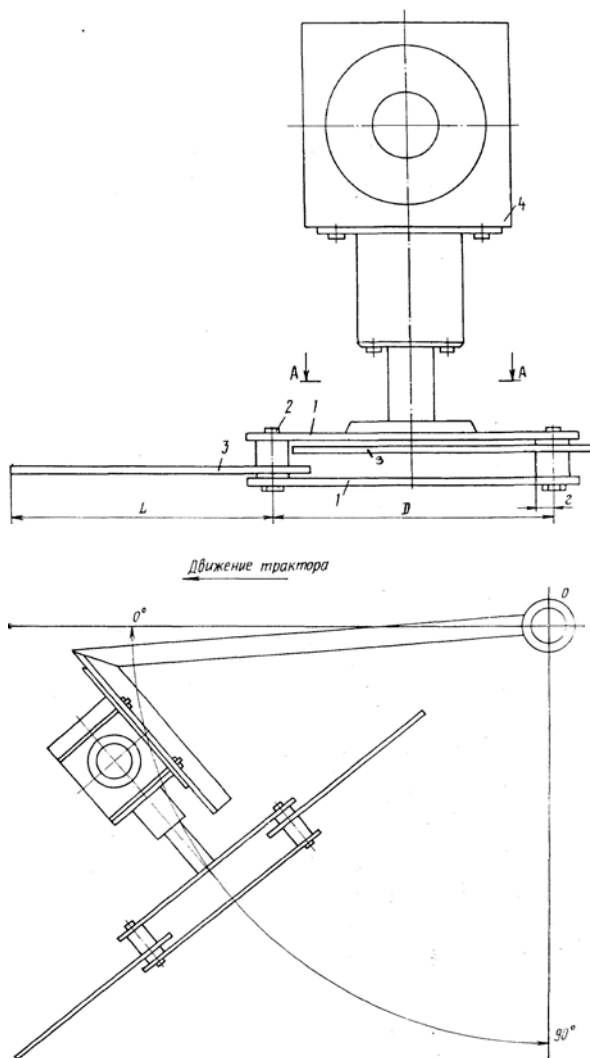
Схема роторного кустореза со смещенными ножами: 1 – корпус; 2 – опорные оси; 3 – ножи; 4 – редуктор
